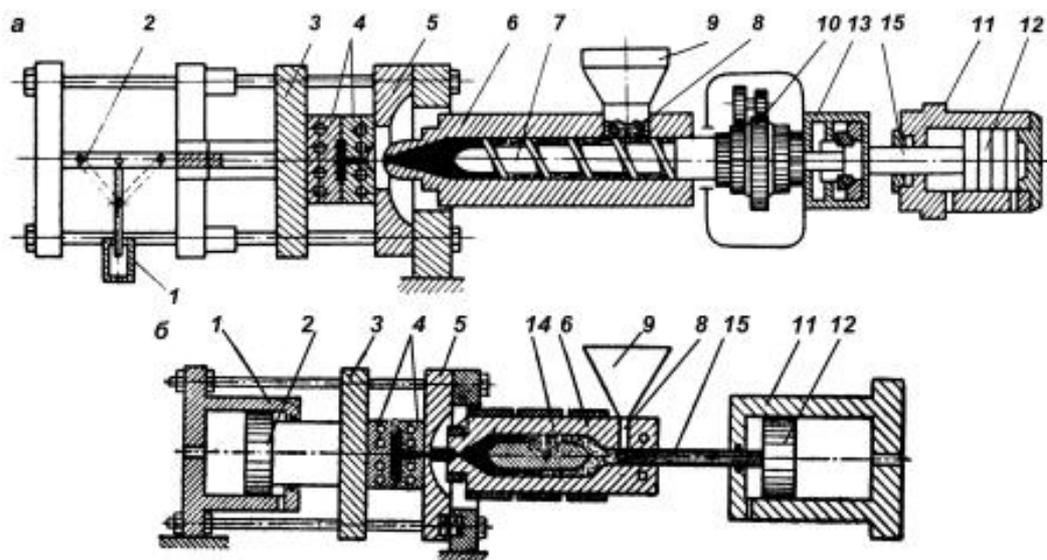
Схема литьевой машины со шнековой (а) и плунжерной (б) пластикацией расплава: 1 – гидроцилиндр механизма смыкания; 2 – поршень гидроцилиндра механизма смыкания; 3 – подвижная плита; 4 – полуформы; 5 – неподвижная плита; 6 – пластикационный цилиндр; 7 – шнек; 8 – загрузочное окно цилиндра пластикации; 9 – бункер; 10 – привод шнека; 11 – корпус гидроцилиндра механизма впрыска; 12 – поршень гидроцилиндра впрыска; 13 – гидроцилиндр шнека; 14 – торпеда – рассекатель потока расплава; 15 – плунжер.
